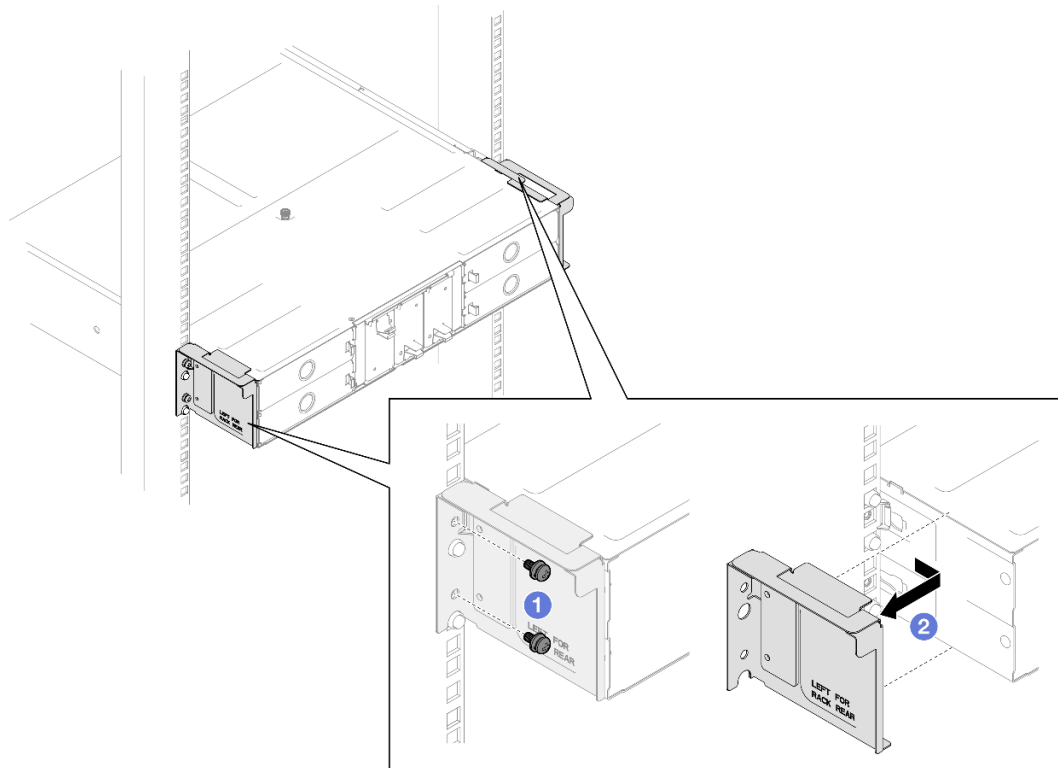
Remoção de suportes de remessa para racks com profundidade de 29,5 polegadas
